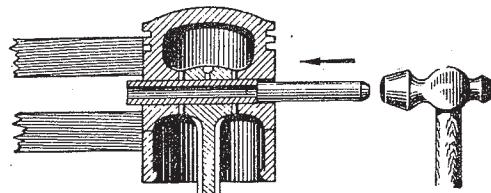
Выпрессовка пальца с помощью металлического стержня и молотка
